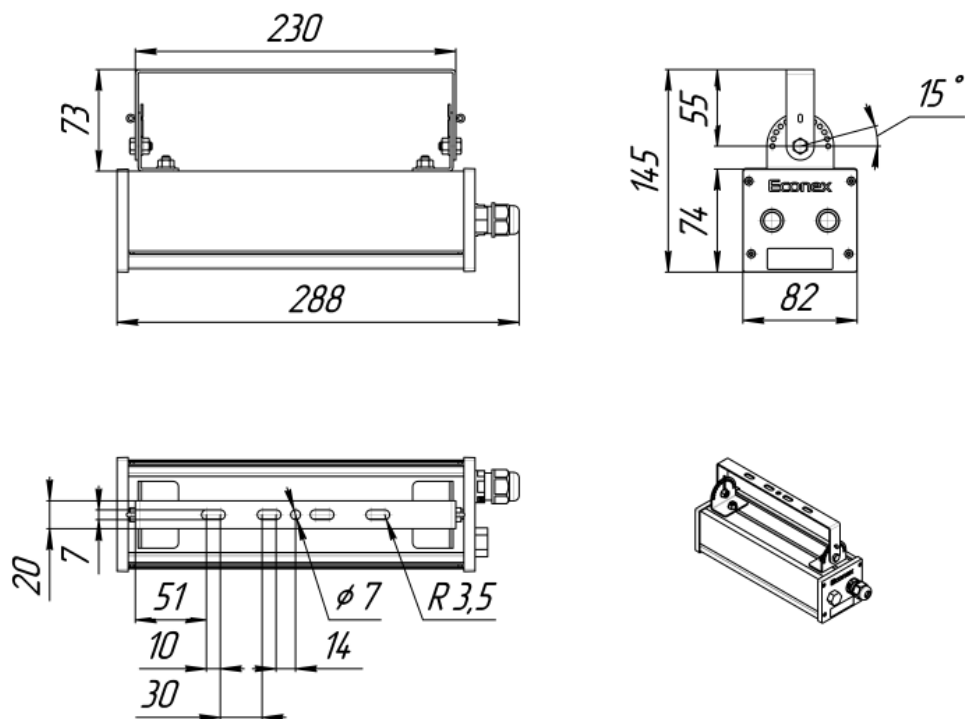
Габаритный чертёж светильника Econex Board G2
